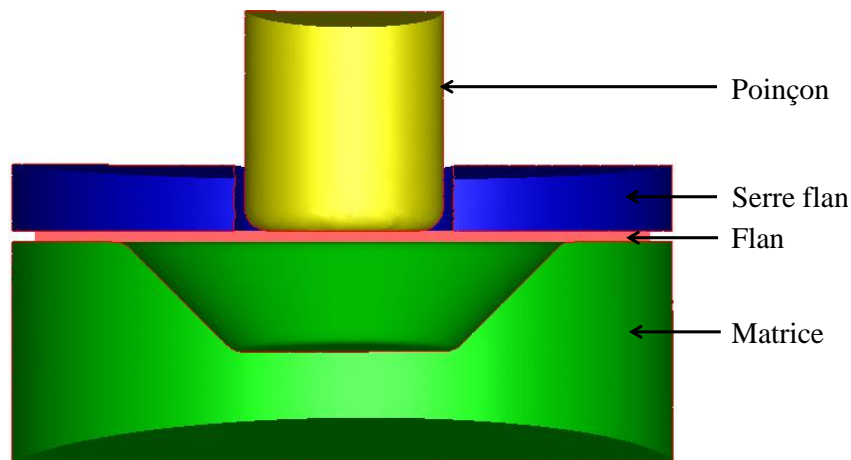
Vue en coupe de l'ensemble du procédé d'emboutissage
